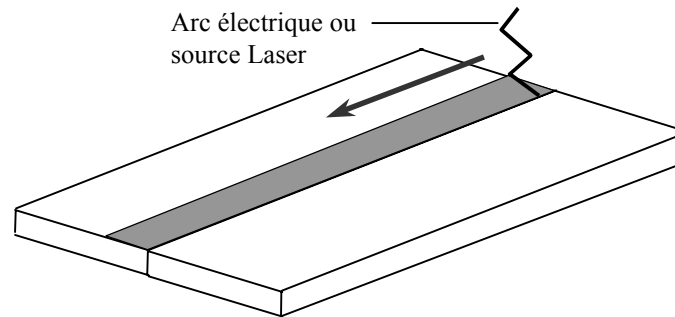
Configuration de soudage avec un dépôt de flux unilatéral
